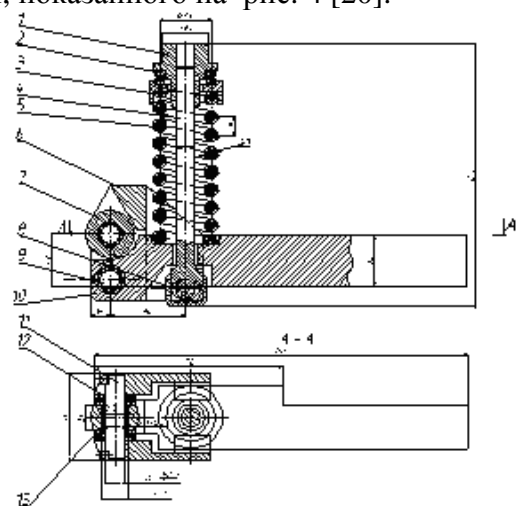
Конструктивная схема устройства для обкатывания деталей торообразным роликом со стабилизацией рабочего усилия обкатывания
